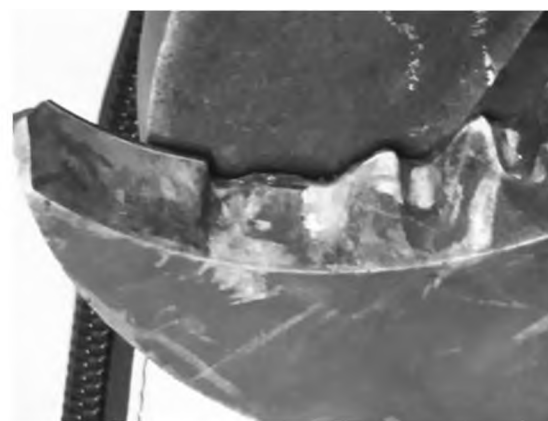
Износ режущей части гидравлических кусачек (Вид дефекта: скол режущей части)
